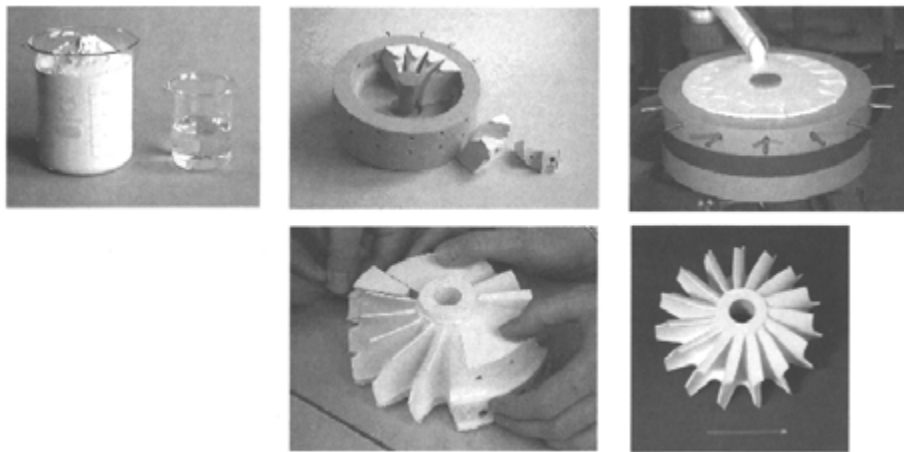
COULAGE D'UNE PIÈCE CÉRAMIQUE À FORME COMPLEXE PAR DCC
